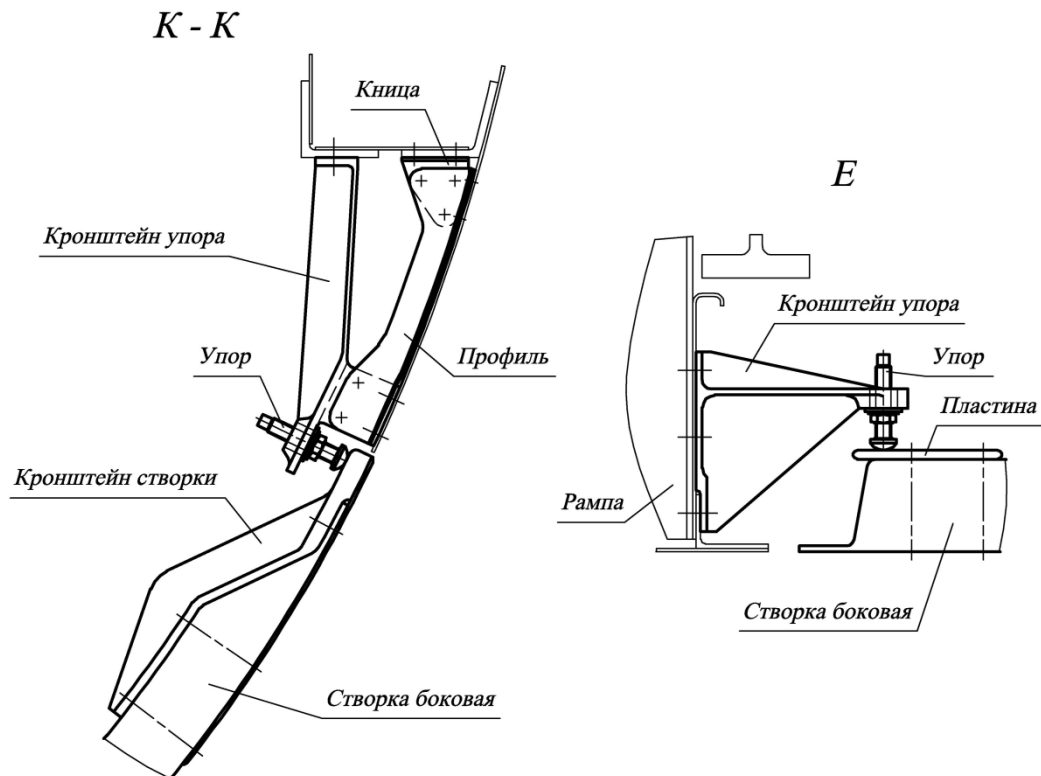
Схема регулировки положения боковых и средней створок в закрытом положении
